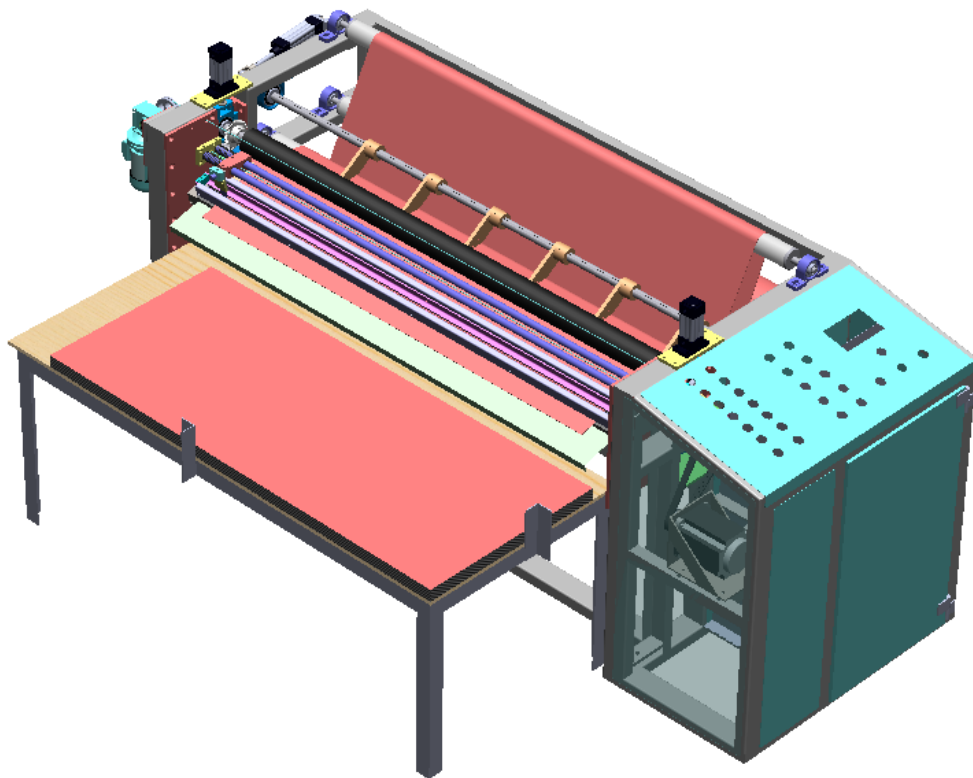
Ensamble - máquina cortadora (Imagen frontal).
